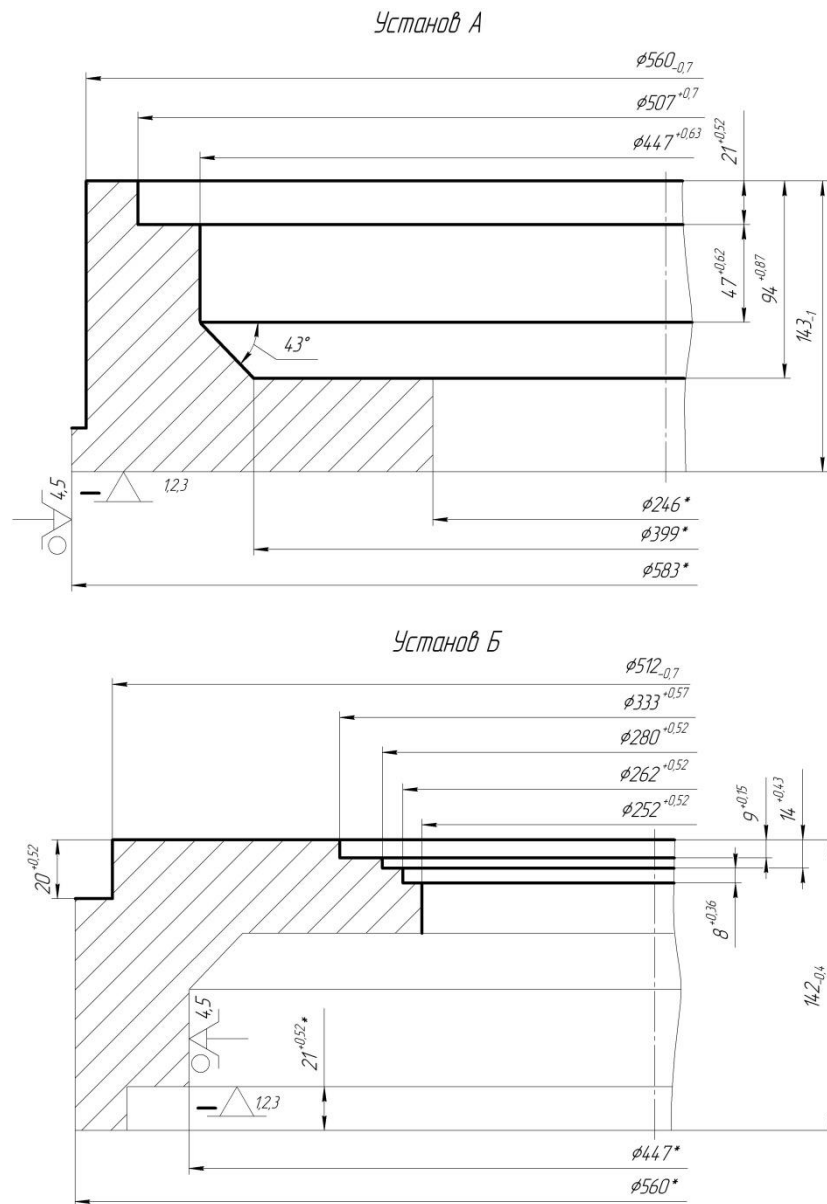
Схема базування заготовки на токарній операції (перший варіант)
